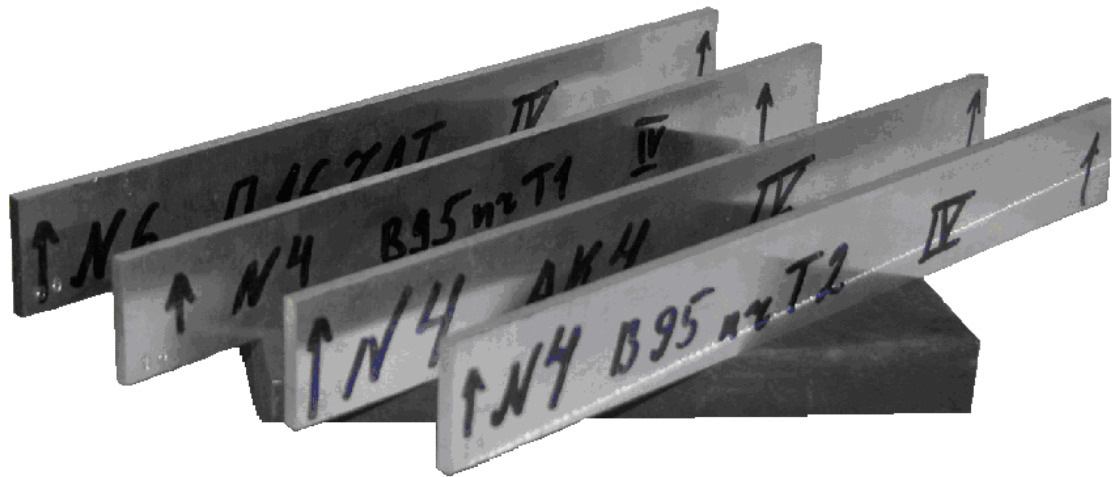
Образцы-пластины для тарировки процесса раскатки
